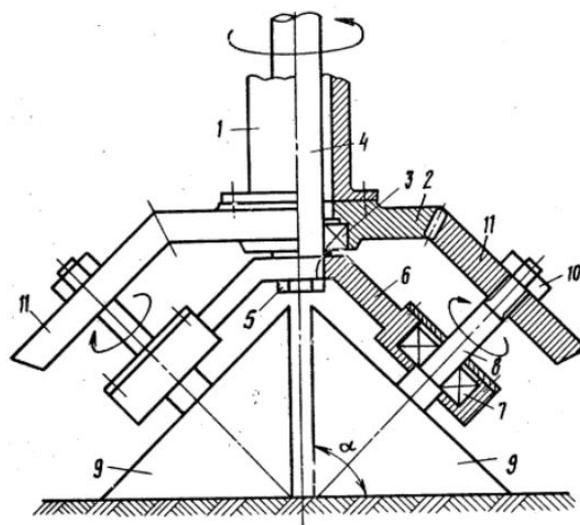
Устройство для уплотнения грунта: 1 – неподвижный корпус; 2 – зубчатый венец; 3, 7 – подшипник; 4 – приводной вал; 5 – болт; 6 – траверса; 8 – ось; 9 – конический элемент; 10 – гайка; 11 – коническая шестерня
